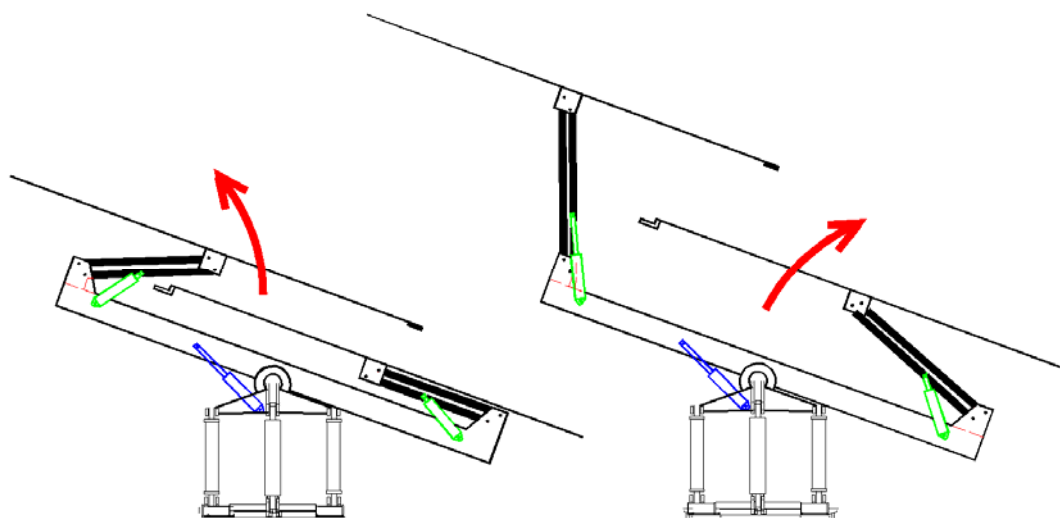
Процесс перехода отвала из транспортировочного положения.
